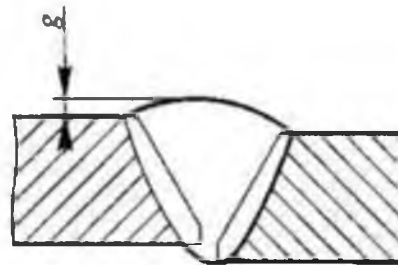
Вимірювання випуклості стикового шва (g) у разі різного рівня зовнішніх поверхонь деталей, спричиненого зміщенням під час складання з'єднання для зварювання.
